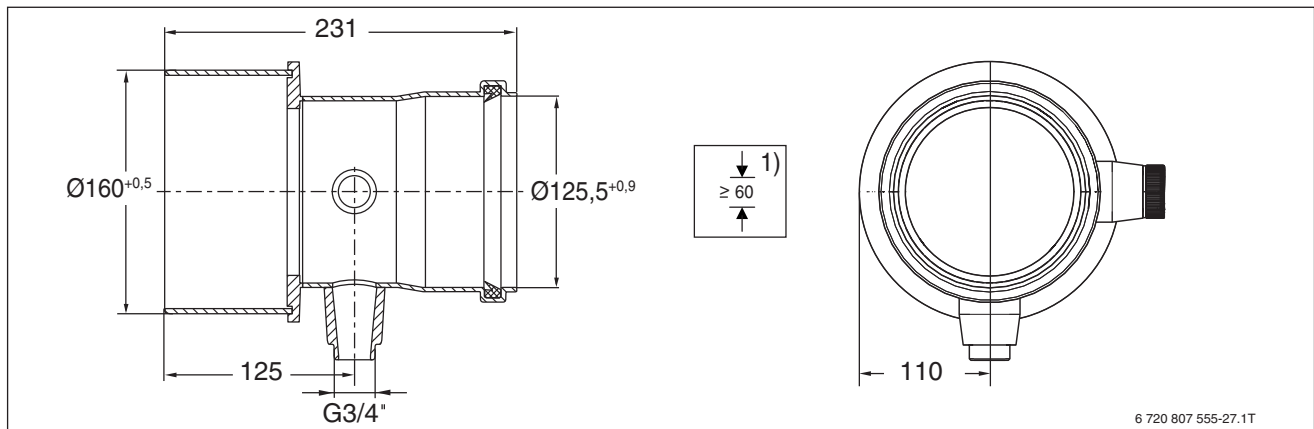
Anschlussrohr DN 160/125 (Maße in mm)
